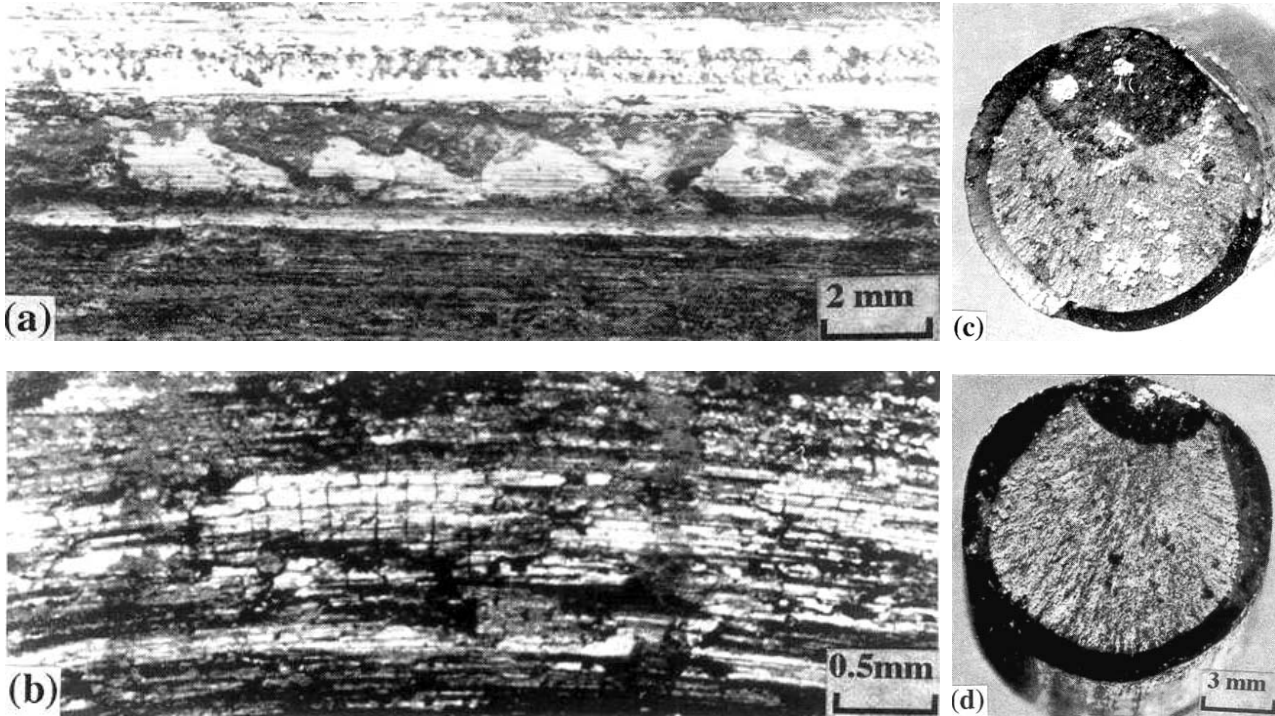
Pre-stressed concrete steel cable, Chafe zone인 Martensite
